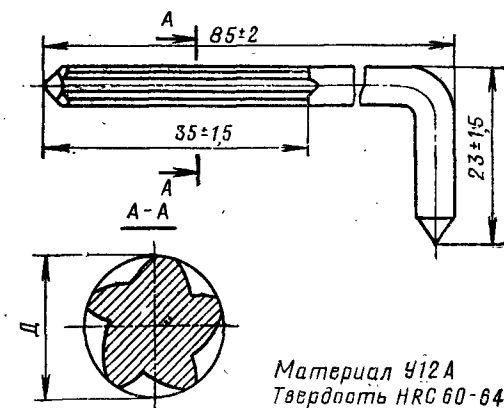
Металлическая развертка для снятия порохового нагара со стенок газоотводных отверстий
